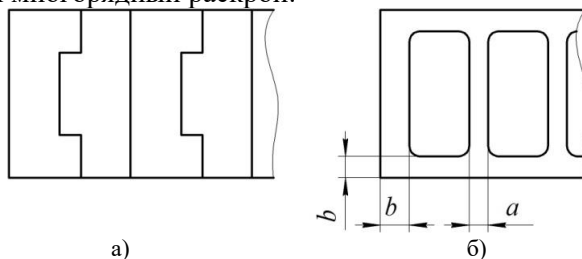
Примеры раскроя металла: а – безотходный раскрой; б – раскрой с отходом
